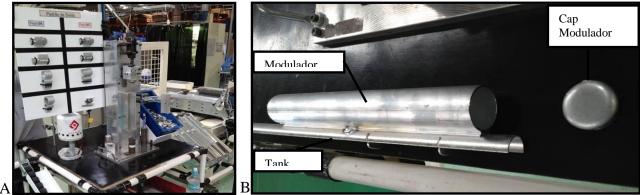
(A) Dispositivo de inserção do cap modulador. (B) Figura com o cap modulador e modulador antes da operação de inserção.
